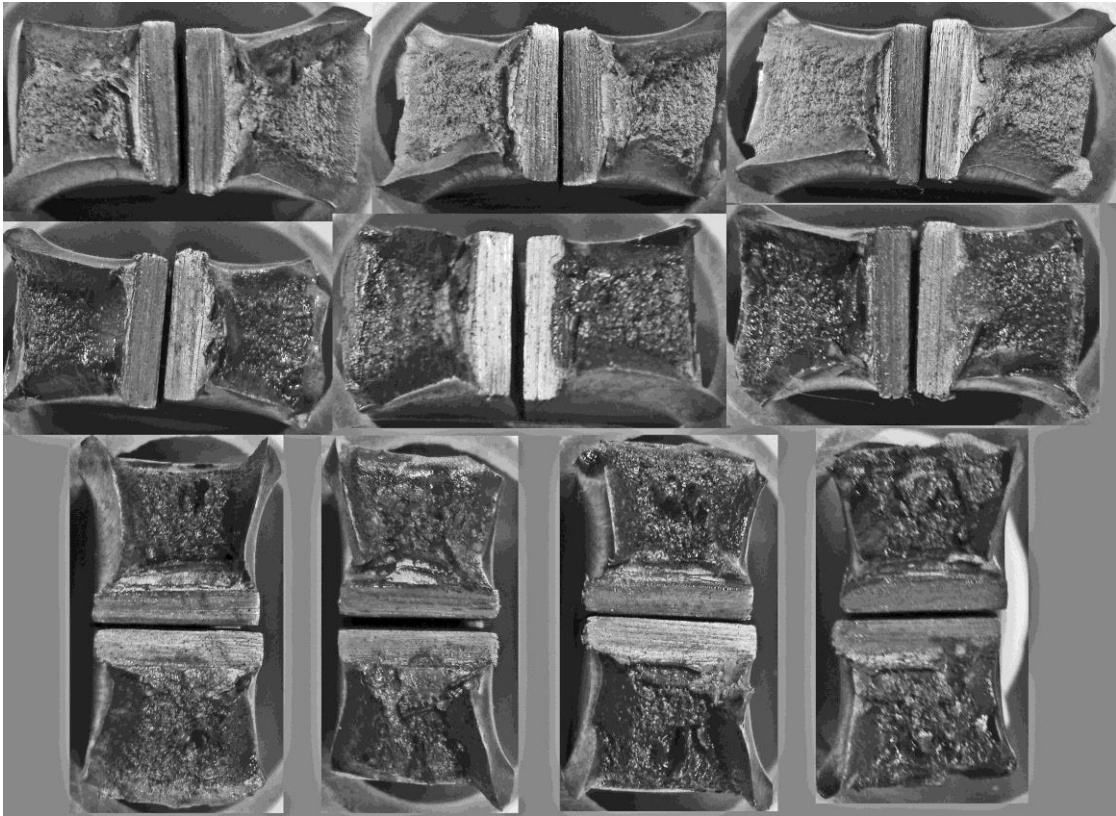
Fotografias das superfícies de fratura do ensaio Charpy-V, dos corpos de prova soldados com 100 °C de pré-aquecimento.
